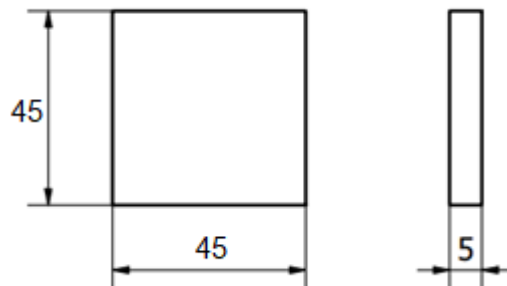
Dimensiones en mm de la probeta para ensayo de pull off (Fuente propia)
